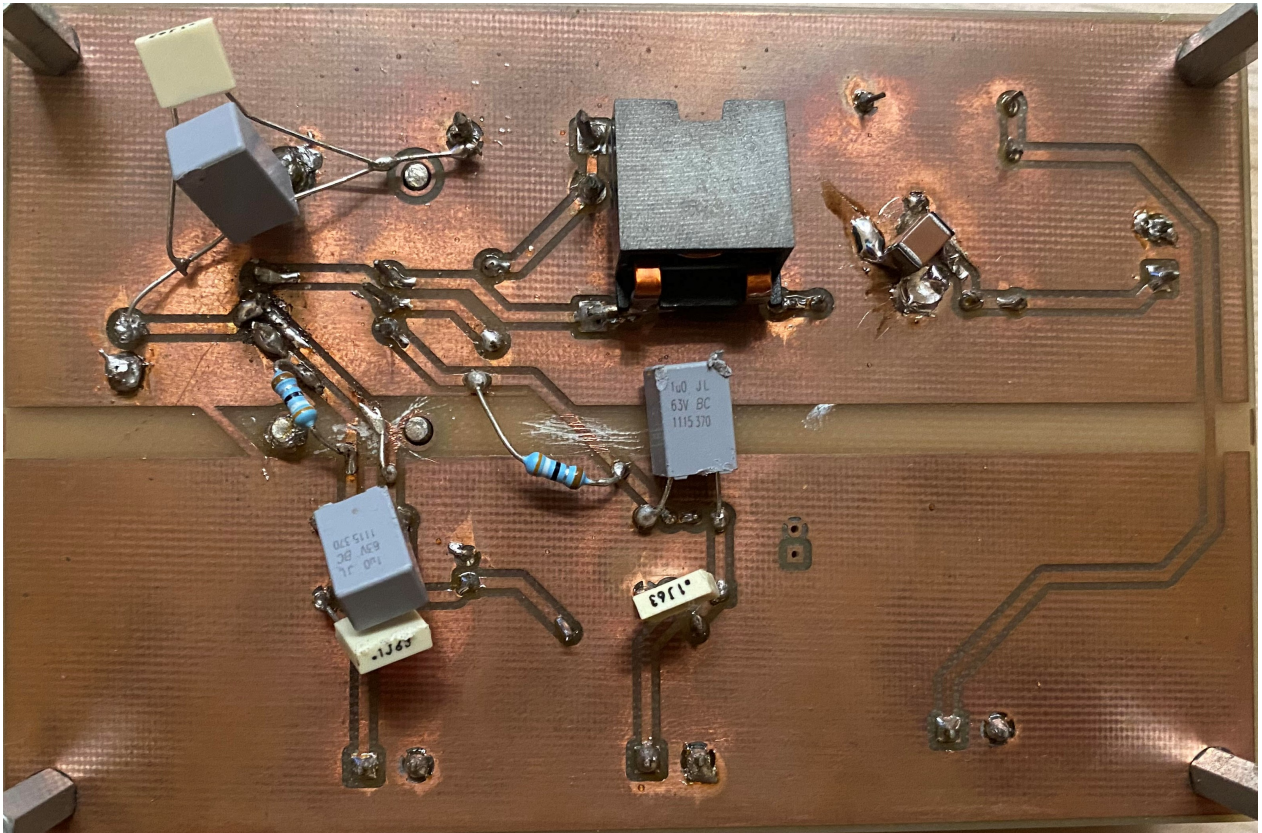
Cara bottom de la PCB amb el nou inductor i condensador
